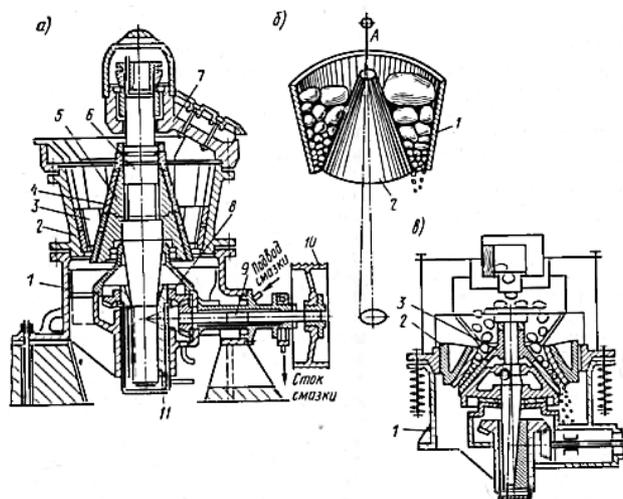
Конусные дробилки: *а)* – с верхней опорой вала; *б)* – схема действия; *в)* – с грибовидной головкой.
